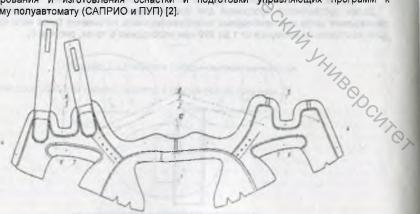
Заготовка полупары верха обуви модели 24142
